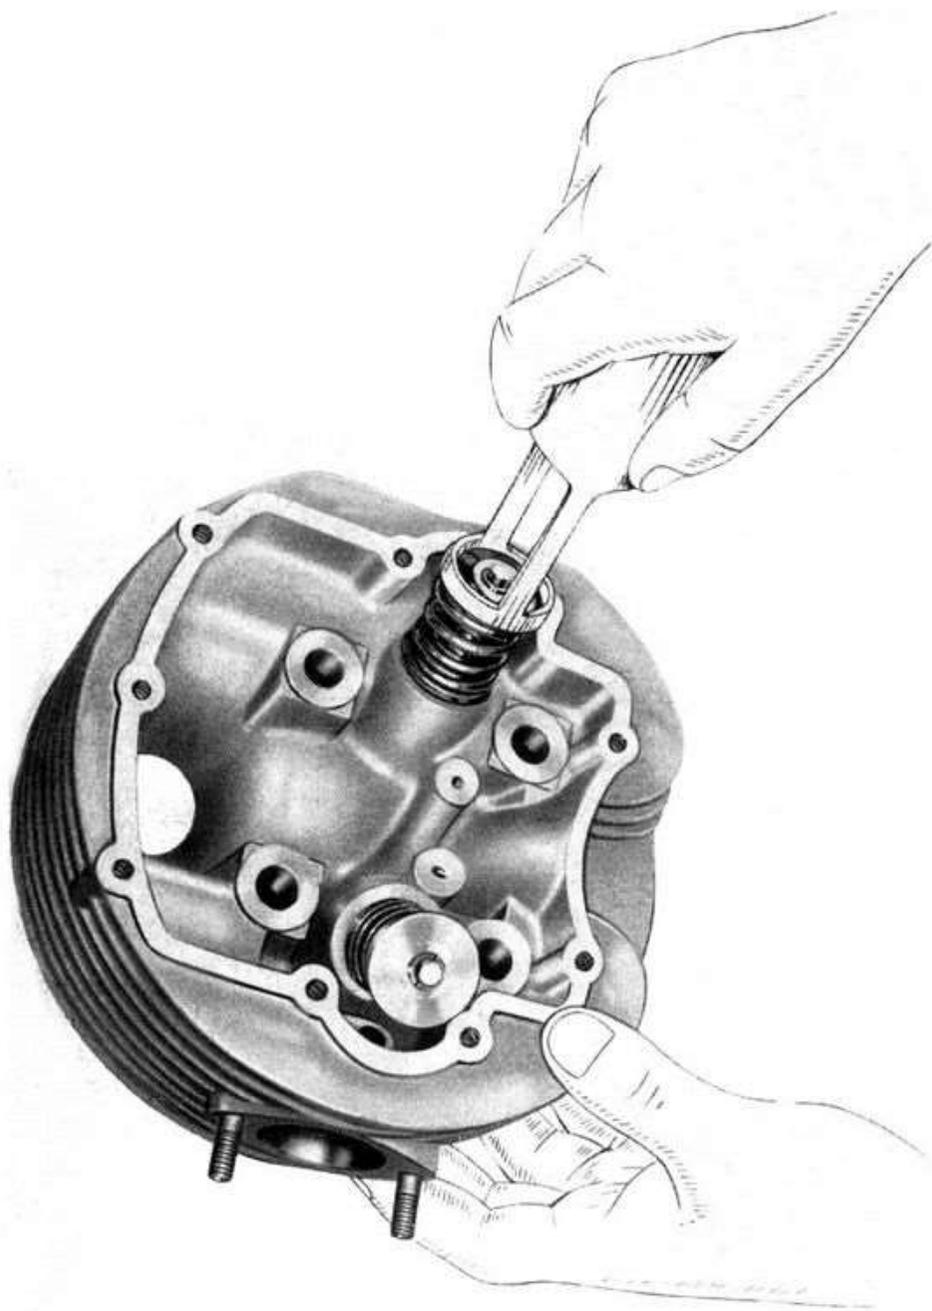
Come vengono compresse le molle per lo smontaggio delle valvole.
